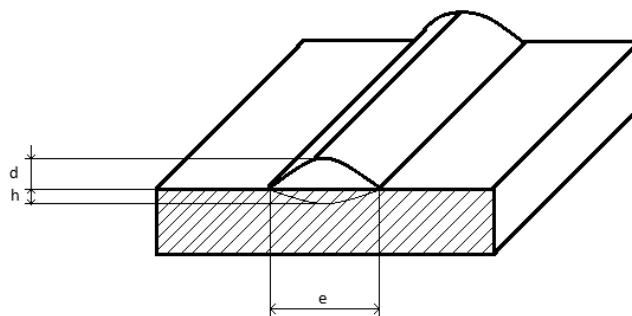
Геометрические размеры наплавленного валика и зоны проплавления
